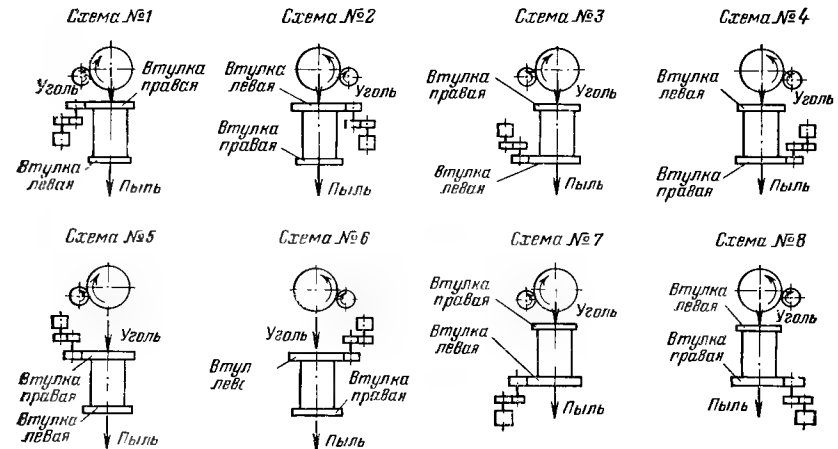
Возможные схемы сборки шаровых барабанных мельниц с редукторным приводом.
